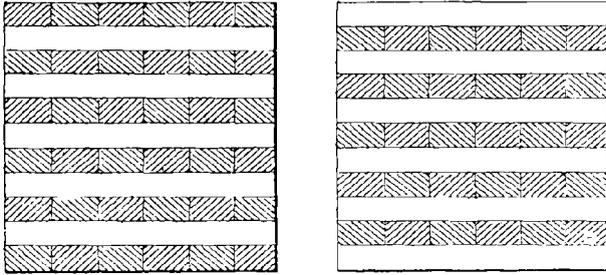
Paquets pour la fabrication des roues pleines en fer forgé.
